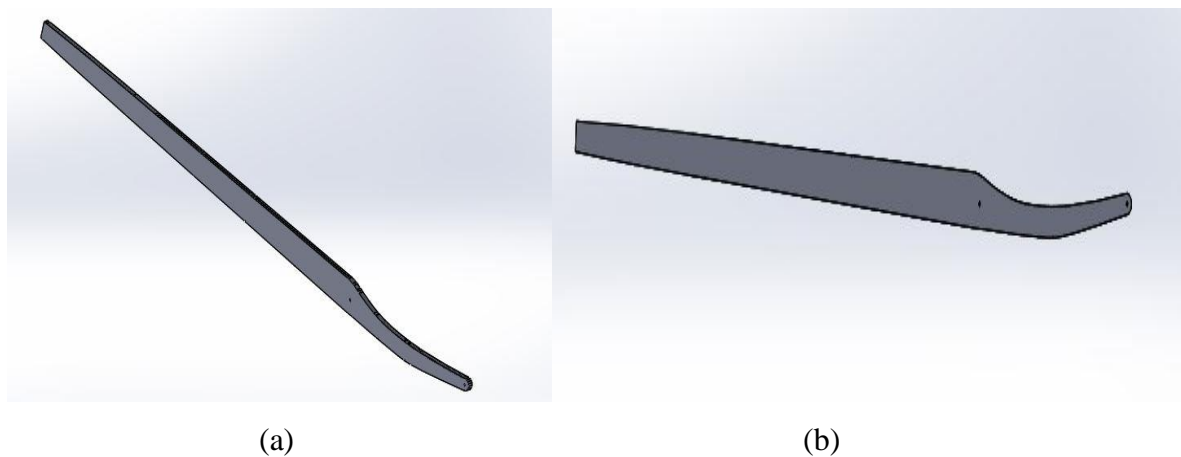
2 (a) Viga principal en vista isométrica, (b) viga principal vista frontal.
